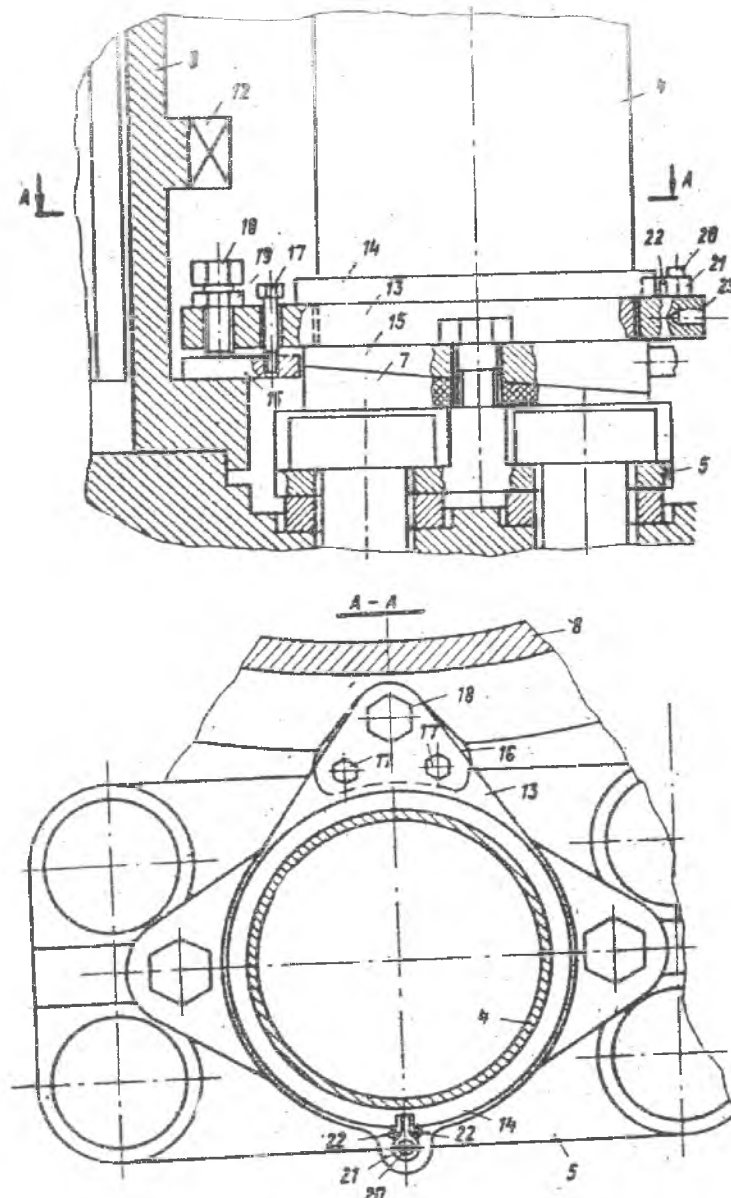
Пристрій для стопорення регулюючої гайки конусної дробарки КМД-2200Т, вигляд А – А
